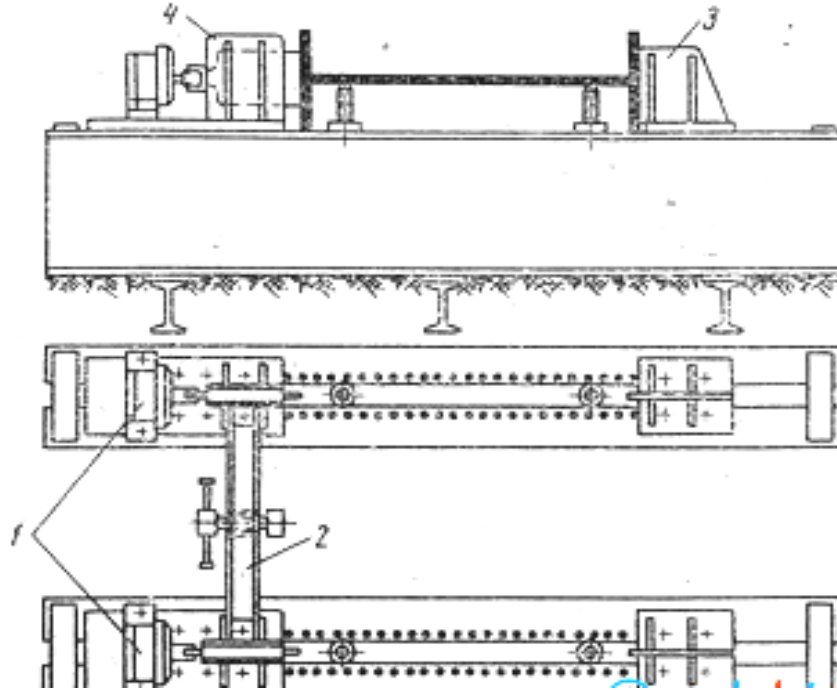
Будова складального кондуктора з пневматичними притисками: 1 – пневматичні циліндри; 2 – переносна траверса; 3 – нерухомий упор; 4 – напрямні рухомого упору
